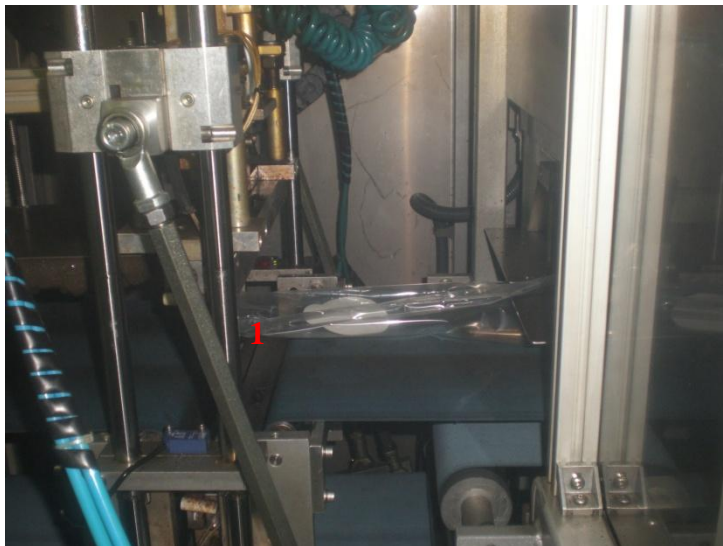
Soldadura (1- selagem do filme) (fotografia tirada pela estagiária)
